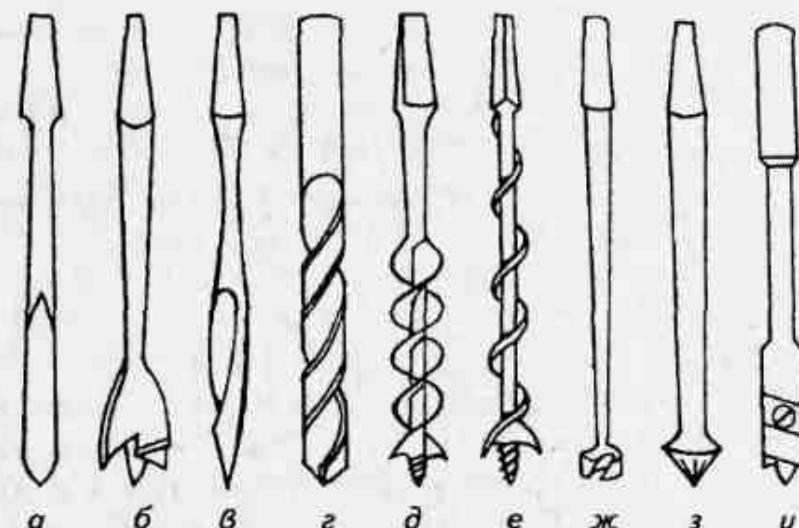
Наиболее распространенные виды сверл: а – ложечное; б – центровое; в – улиткообразное; г – винтовое с конической заточкой; д – винтообразное витое; е – винтообразное шнековое; ж – пробочное; з – зенковочное; и – универсальное (раздвижное)
